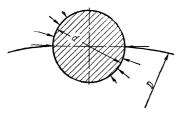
Расчетная схема круглой цилиндрической или конической шпонки
